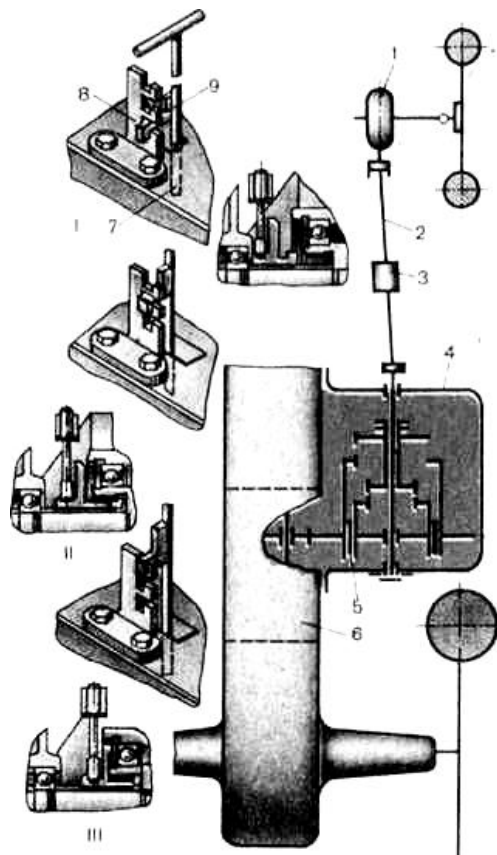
Схема механизмов, передающих крутящий момент на ведущий мост трактора МТЗ-82: 1 - передний мост; 2 - карданный вал; 3 - предохранительная муфта; 4 - раздаточная коробка; 5 - муфта свободного хода; 6 - коробка передач; 7 - тяга управления; 8 - стойка; 9 - упор; I...III - варианты включений.
